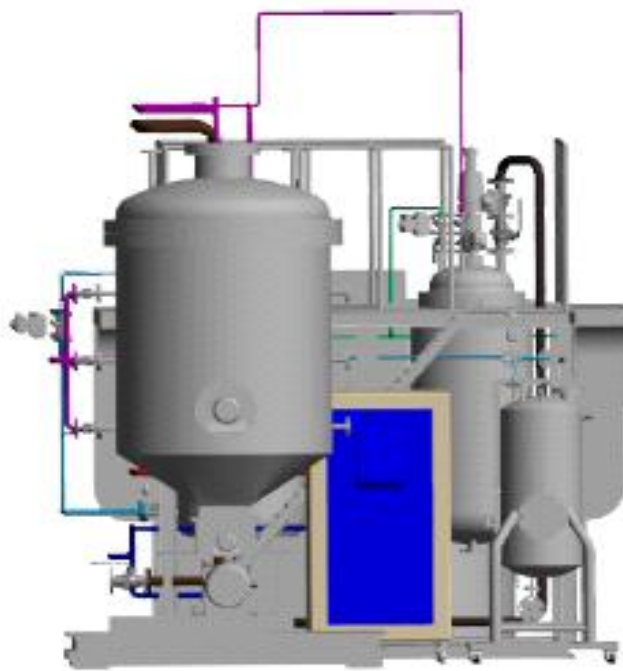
Pilot plant급 수열탄화 시스템3D 설계, 측면도
